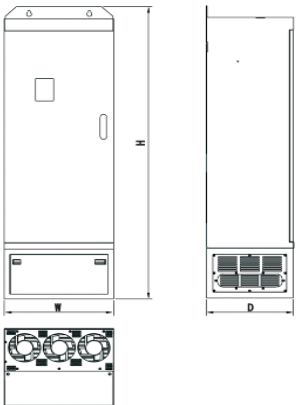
Габаритные размеры (185-315кВт, с базой и без базы)
